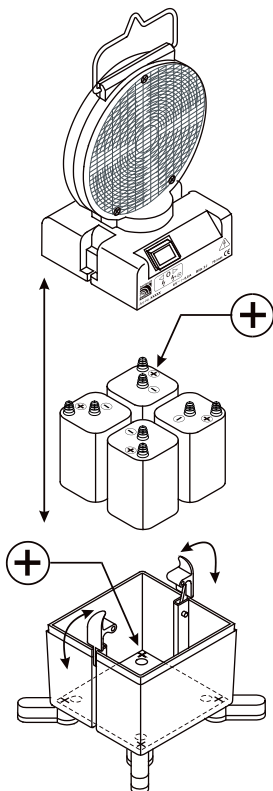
Ersatzteile / Parts / Pieces detachees / Despiece
